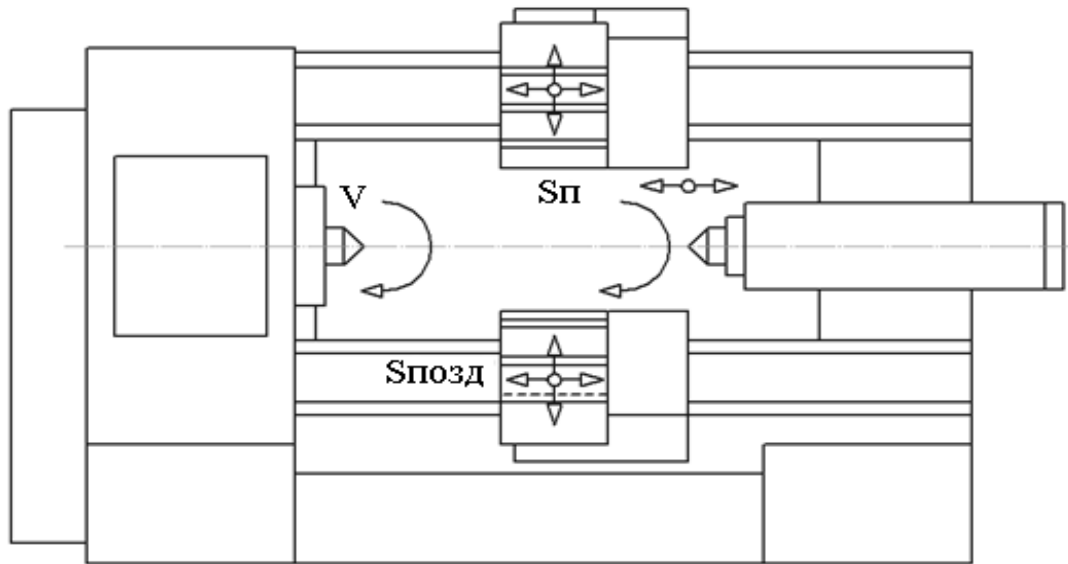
Загальний вид токарного багаторізового напівавтомата
